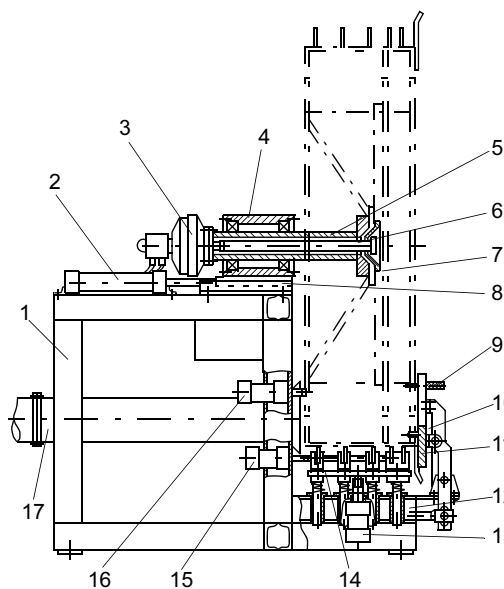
Кондуктор-позиционер для сборки и сварки барабана
